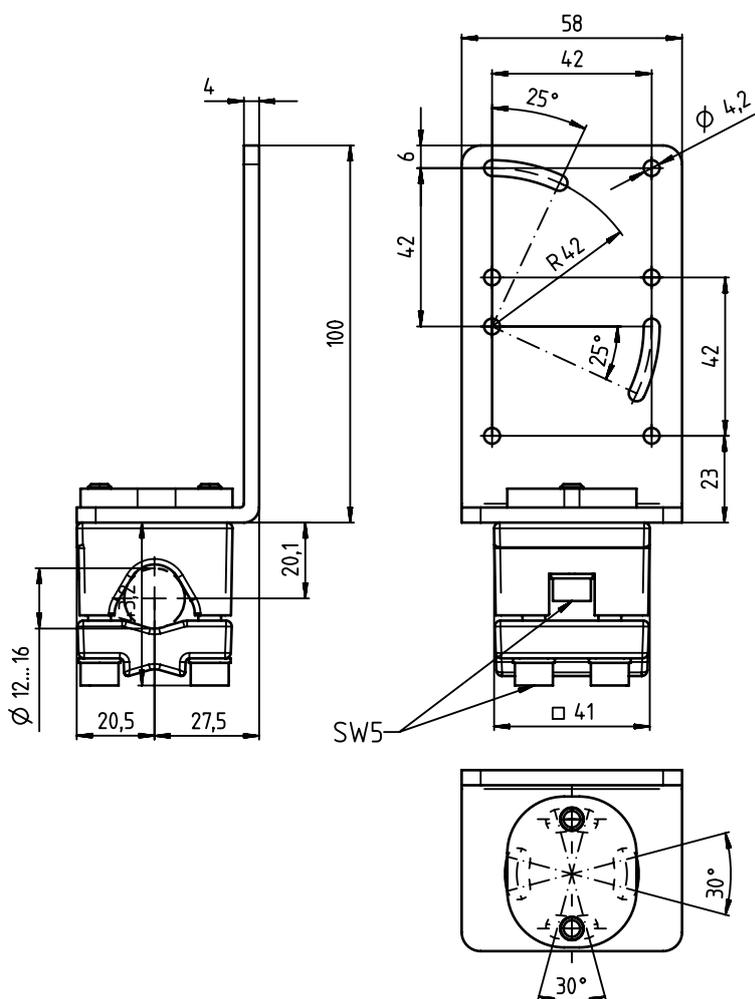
Desenho dimensional do esquadro de fixação BT 300-W
